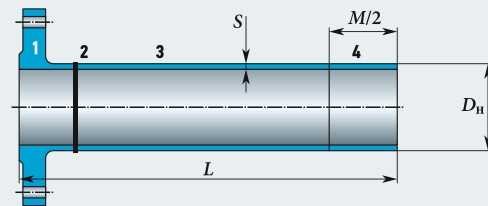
Размеры патрубков «фланец — гладкий конец» (1 — фланец; 2 — сварной шов; 3 — тело патрубка; 4 — калиброванная часть)
